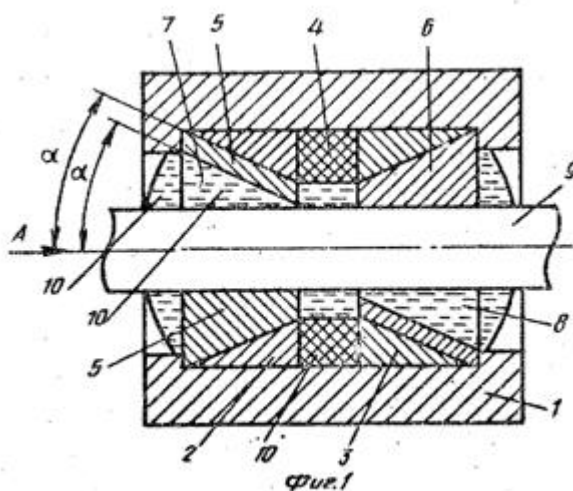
Магнитожидкостный подшипник [39]
